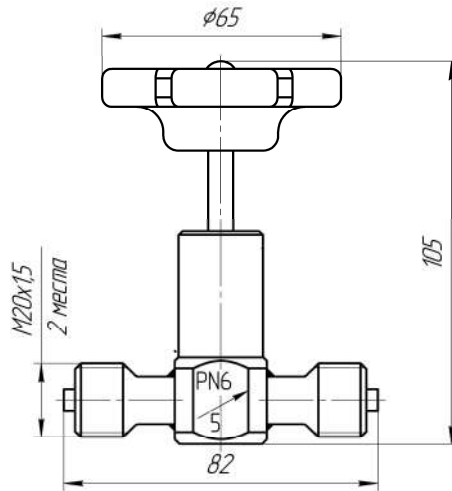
Габаритно-присоединительные размеры ВИГ6С-Н1Б1Б
